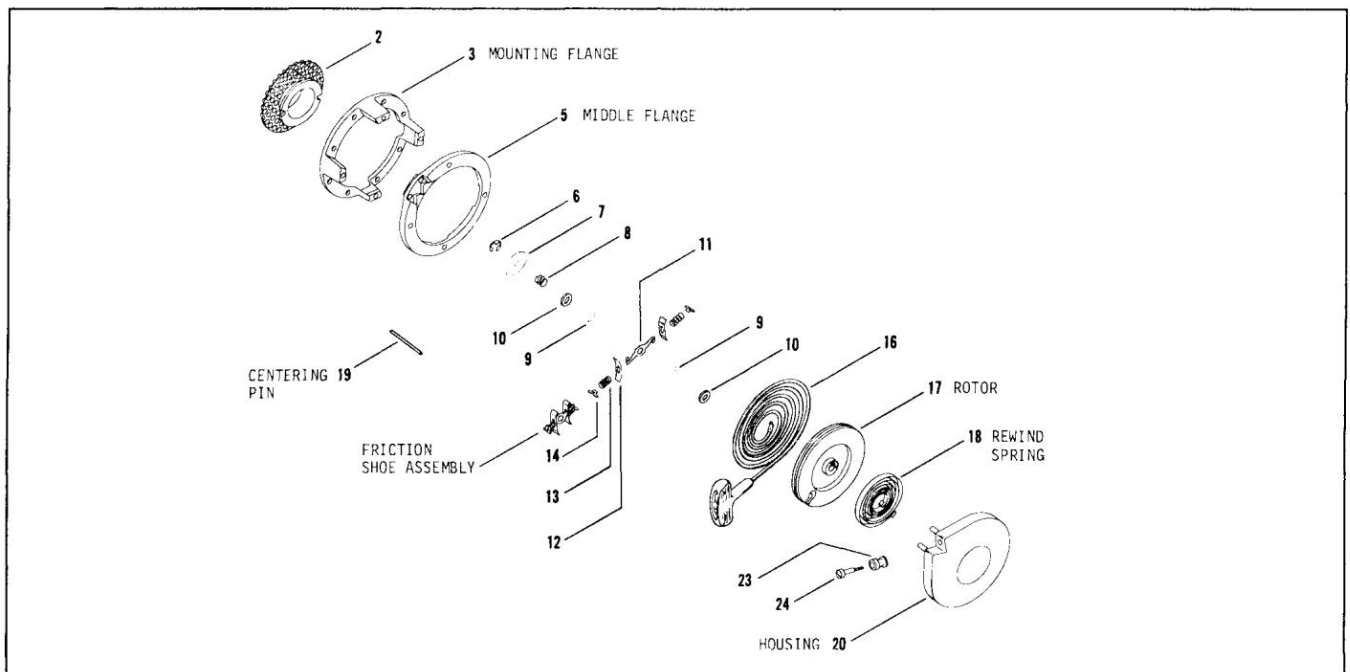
Démarreur Fairbanks-Morse - Vue éclatée.
